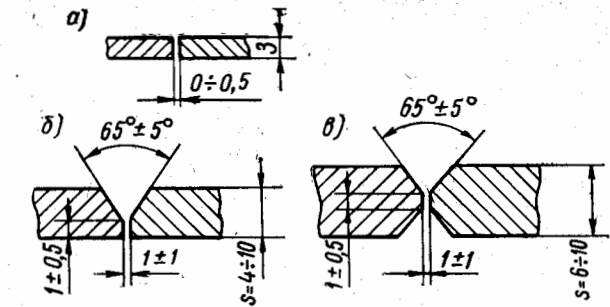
Конструктивные элементы подготовки кромок листового никеля марки НП2 под стыковую ручную аргоно-дуговую сварку (по ОН 26-01-71—68): а — без разделки кромок; б — V-образная разделка кромок; в — X-образная разделка кромок
